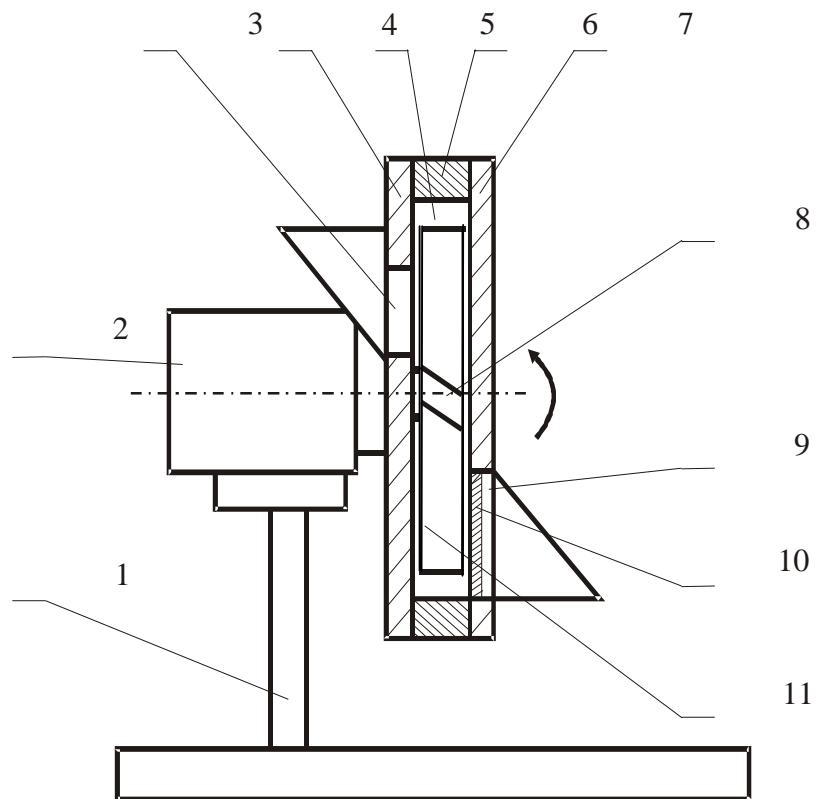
Общий вид дробилки: 1 - рама; 2 – электродвигатель; 3 – загрузочное окно; 4 и 7 – плиты; 5 – камера измельчения; 6 – барабан; 8 – ротор; 9 - выгрузное окно; 10 – решето; 11 – лопасти.
